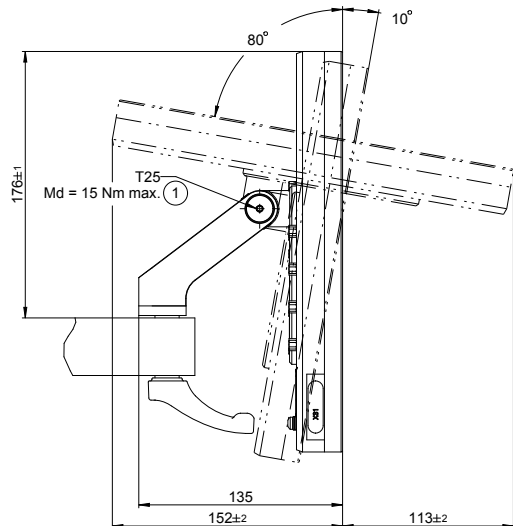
Dimensões do aparelho com suporte Multi-Pos
